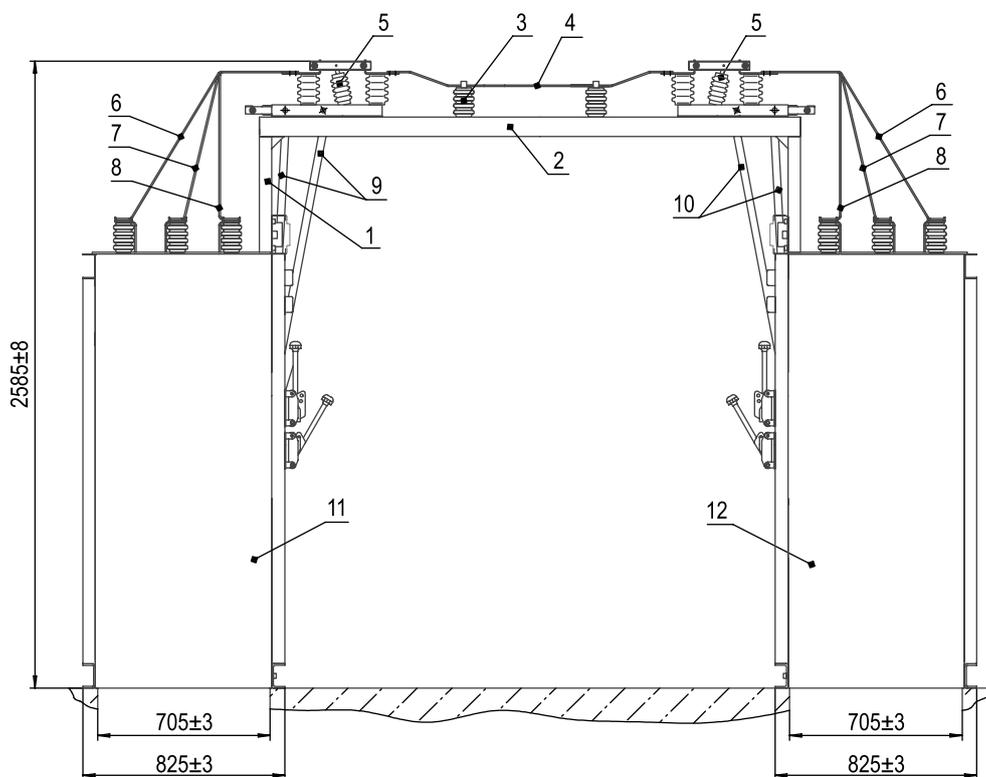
Габаритные, установочные, присоединительные размеры КСО-306 ШВВ:
